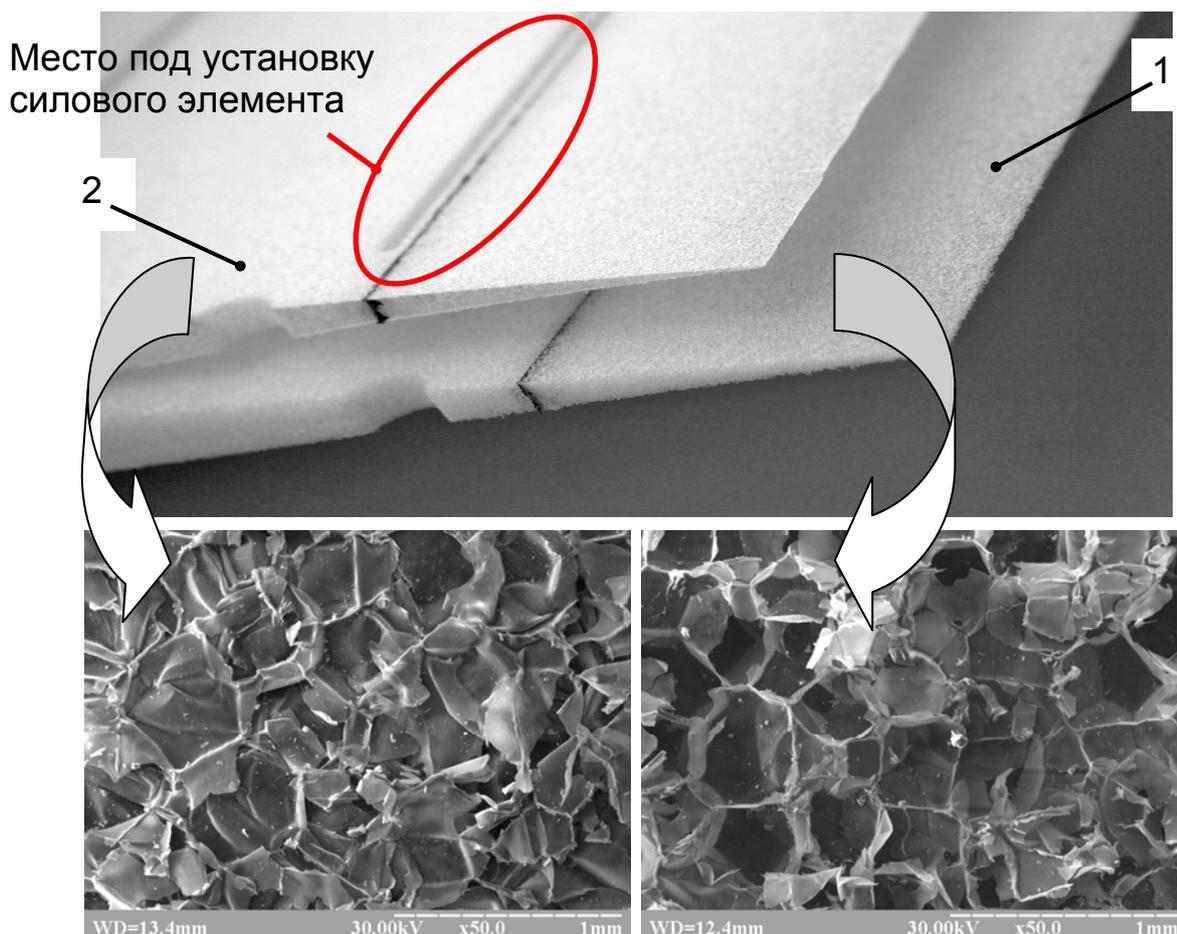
Заготовки из пенопласта и структура поверхности:
